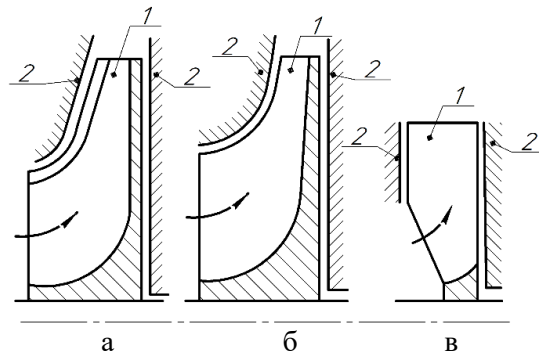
Схематичне зображення проточної частини з робочими колесами різного типу: а – закрите робоче колесо; б – напіввідкрите робоче колесо; в – відкрите робоче колесо; 1 – лопать; 2 – корпус насоса
